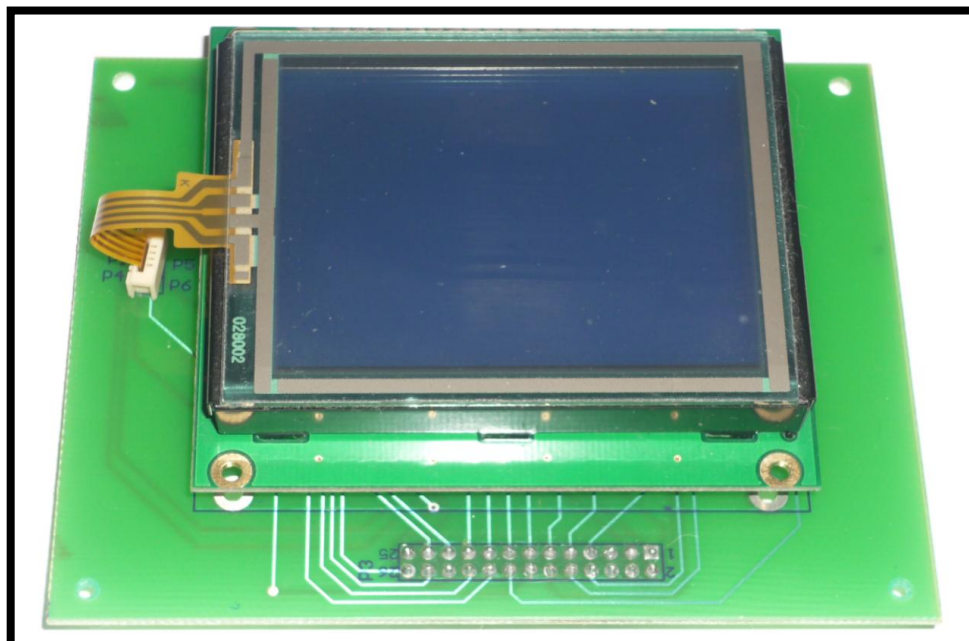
Placa PCB de interfaz con montaje de GLCD.
